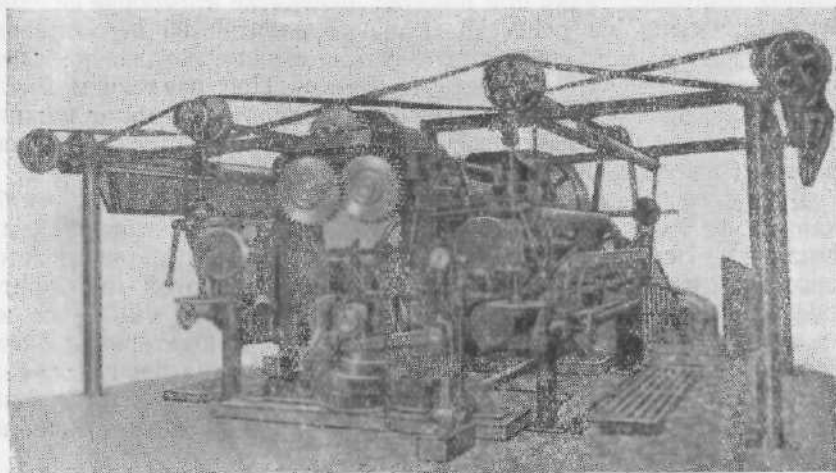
Трехвальный отделочный каток ОК-3/186 (общий вид)
